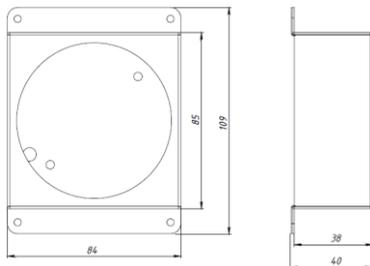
Габаритные размеры Geniled Griliato Tetrис Gx53.
